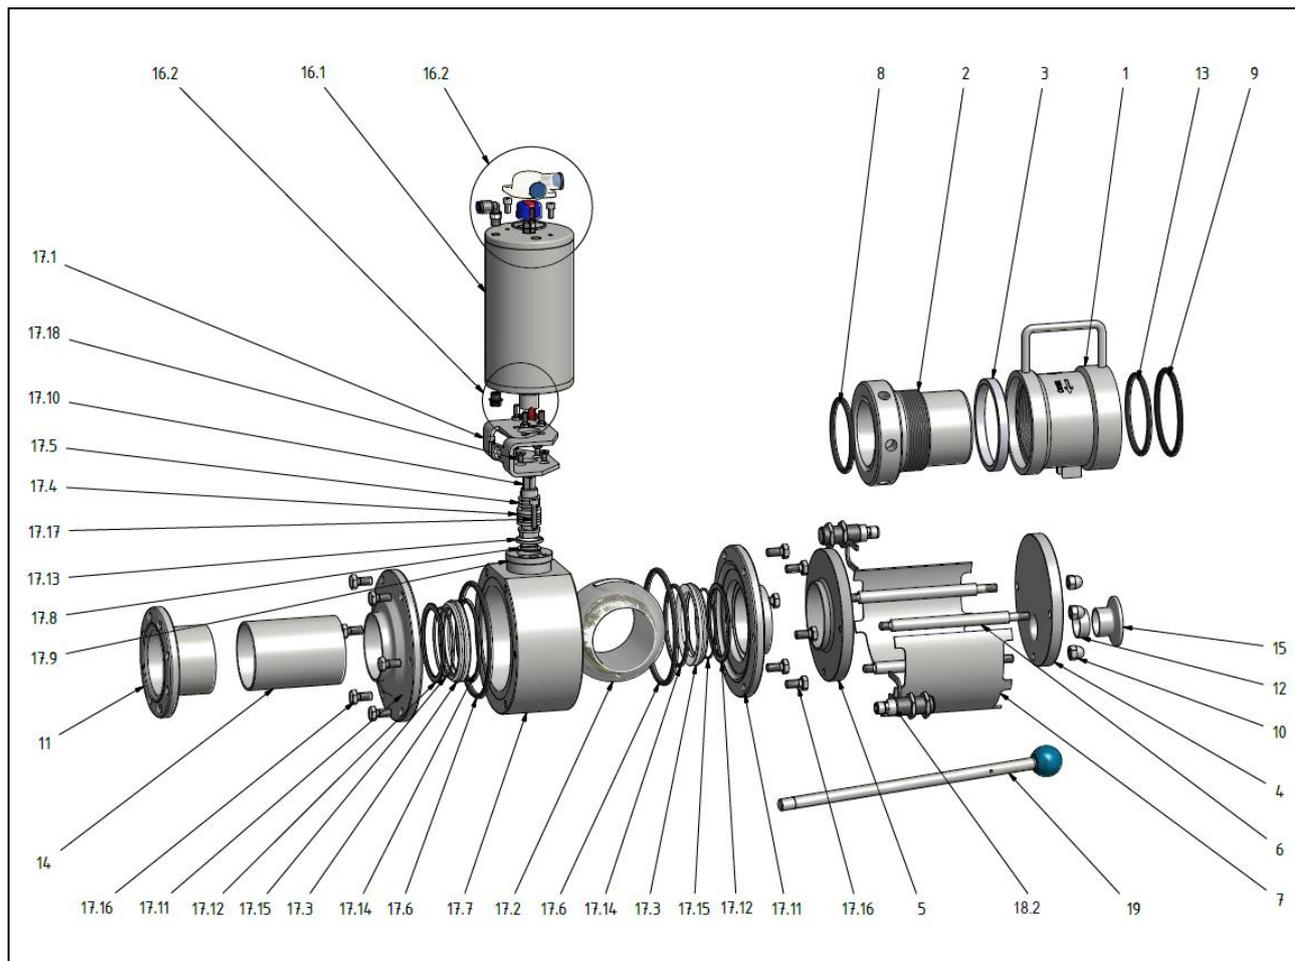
Aufbau Steckkammer mit Kugelventil
